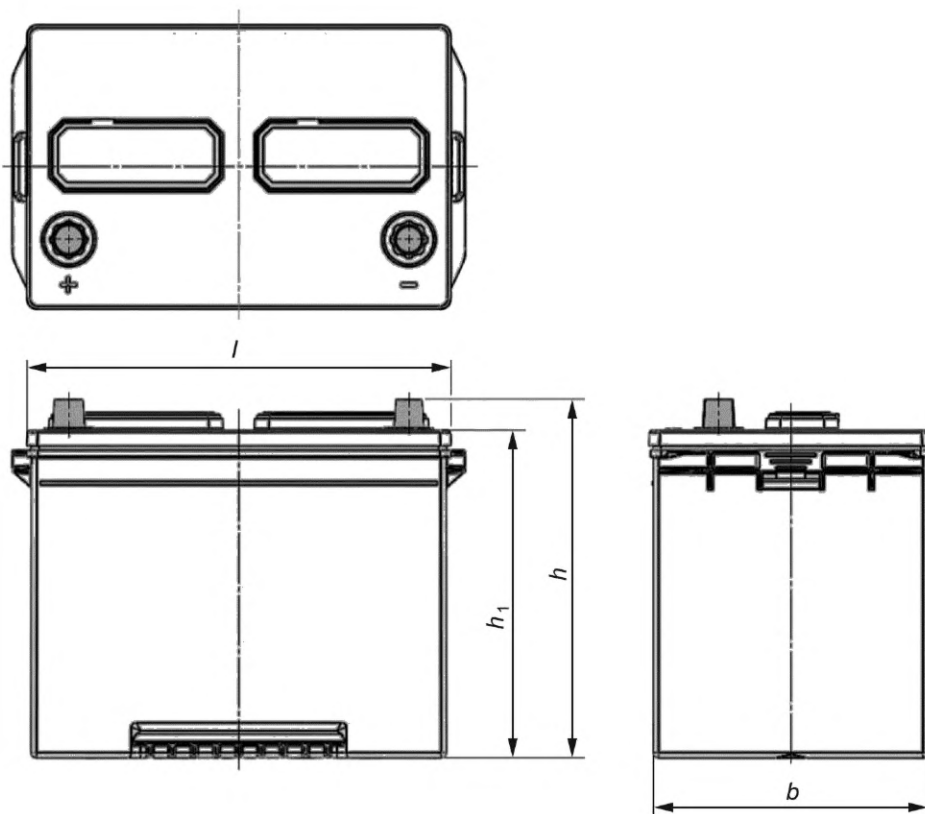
Основные размеры батарей типоразмеров 24, 25, 26, 27, 34, 51, 86
